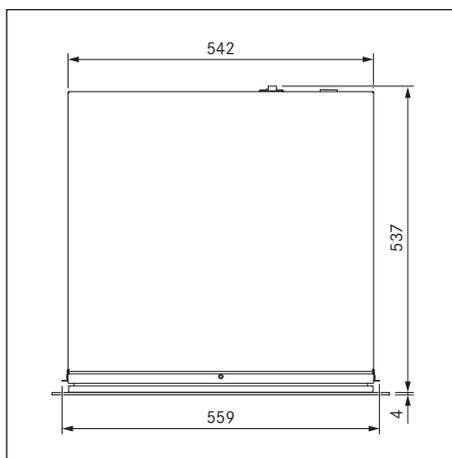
Dimensions MSS290 - Vue de dessus
